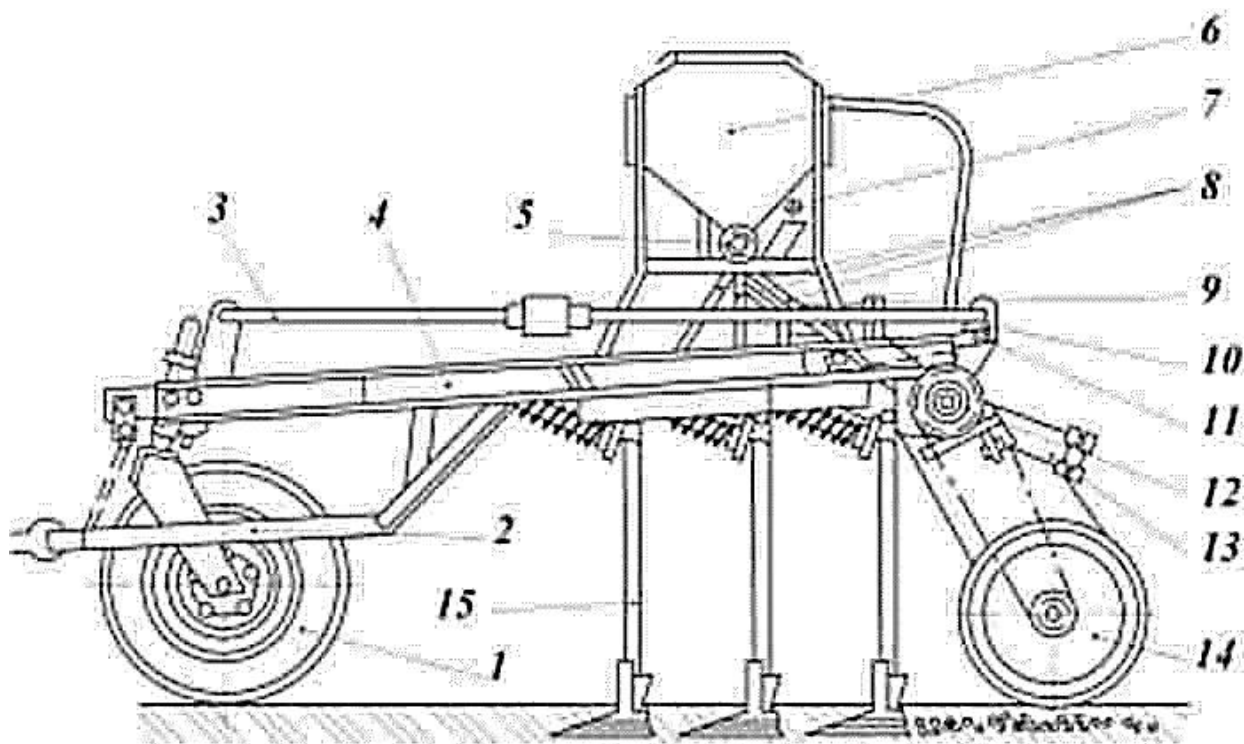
Стерневая сеялка СЗС-2,1: 1 – колесо; 2 – прицепное устройство; 3 – тяга; 4 – рама; 5 – зерновой высевающий аппарат; 6 – семенной бункер; 7 – туковывсевающий аппарат; 8 – семяпроводы; 9 – механизм подъема; 10 – кронштейн; 11 – планка; 12 – механизм привода; 13 – рамка; 14 – кольчатый каток; 15 – сошник
